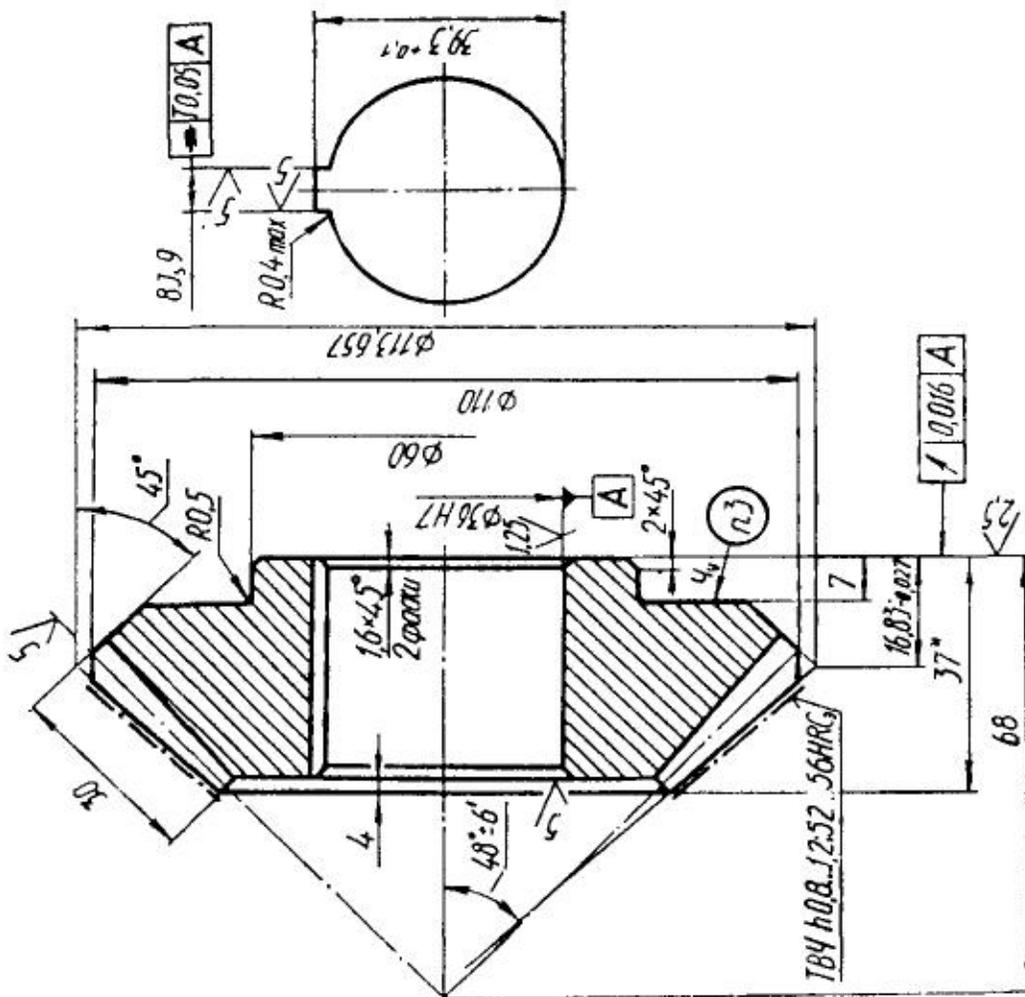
Креслення конічного зубчастого колеса зі зображенням робочого профілю зуба.
